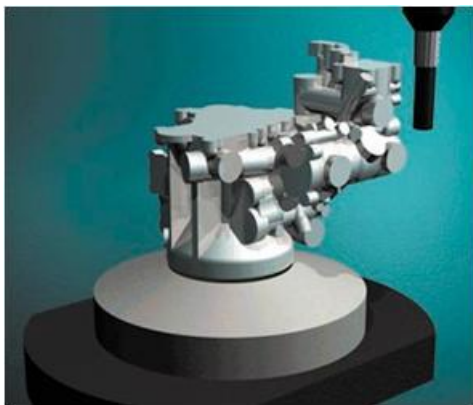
п'ятиосьова обробка дозволяє обробити всю деталь за один або два установи.
